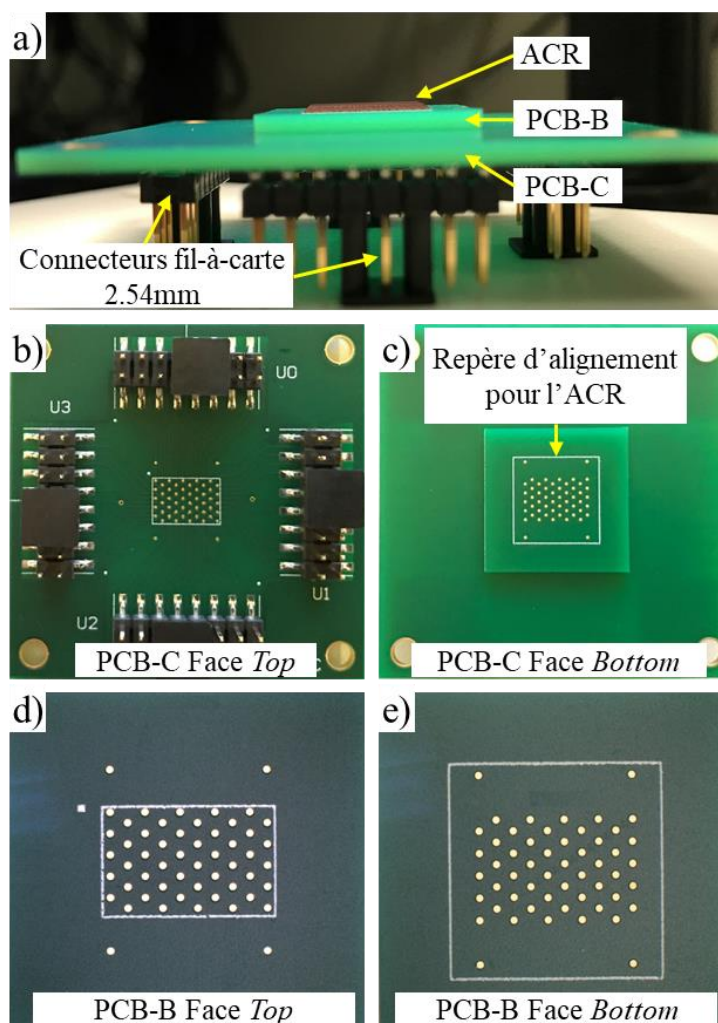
D. 3. a) Capteur : assemblage du PCB-C, PCB-B et le matériau ACR, b) face *Top* du PCB-C, c) face *Bottom* du PCB-C avec le PCB-B soudé par-dessus, d) face *Top* du PCB-B, e) face *Bottom* du PCB-B
